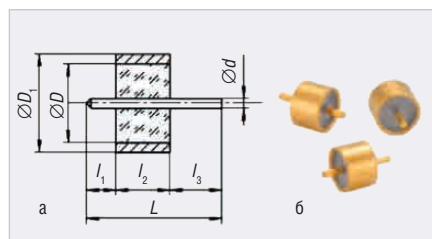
Конструкция СВЧ-ввода (а) и его внешний вид (б)
